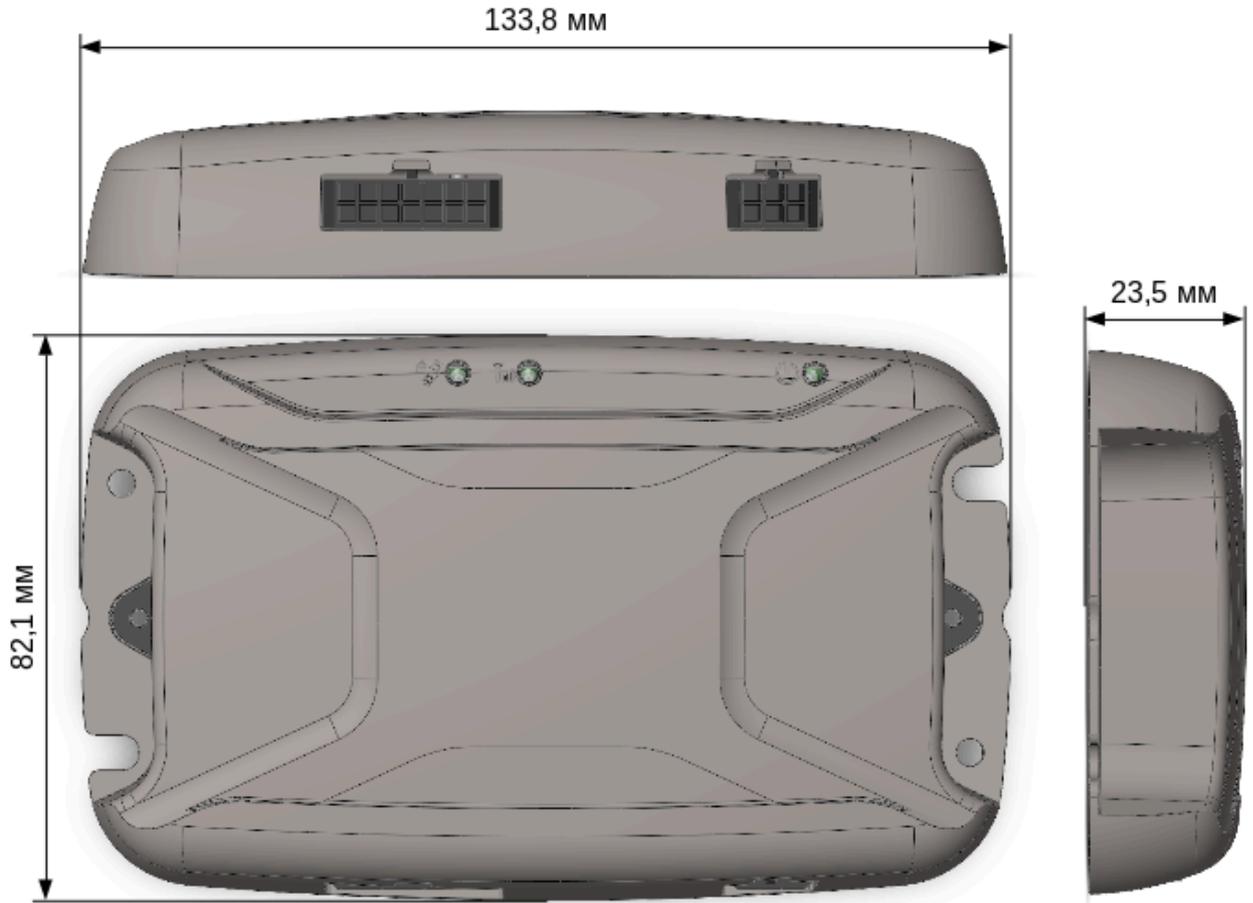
Внешний вид корпуса основного блока и габаритные размеры.
